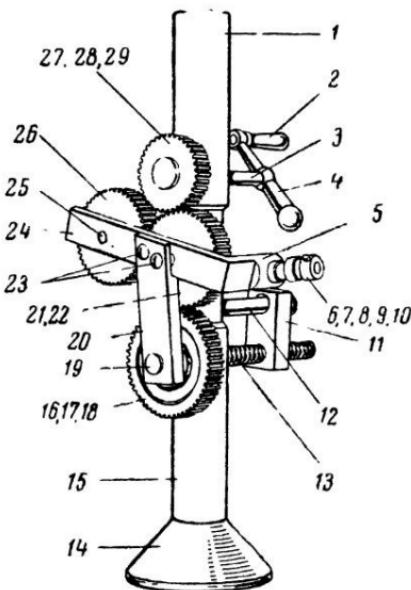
Модель механизма подачи суппорта токарного станка: 1, 15 — стойка; 2 — ручка привода; 3 — «шпиндель»; 4 — рычаг ручки привода; 5 — кронштейн; 6 — гильза; 7 — конусная шпилька; 8 — втулка; 9 — пружина; 10 — фиксатор; 11 — «суппорт»; 12 — направляющая «суппорта»; 13 — «ходовой винт»; 14 — основание; 16 — зубчатое колесо; 17 — стопорное кольцо; 18 — стопорный винт; 19 — винт крепления «трензеля»; 20 — планка; 21 — зубчатое колесо «трензеля»; 22 — ось зубчатого колеса; 23 — винты; 24 — планка; 25 — ось зубчатого колеса; 26 — зубчатое колесо «трензеля»; 27 — ведущее зубчатое колесо «шпинделя»; 28 — шайба; 29 — стопорный винт.
